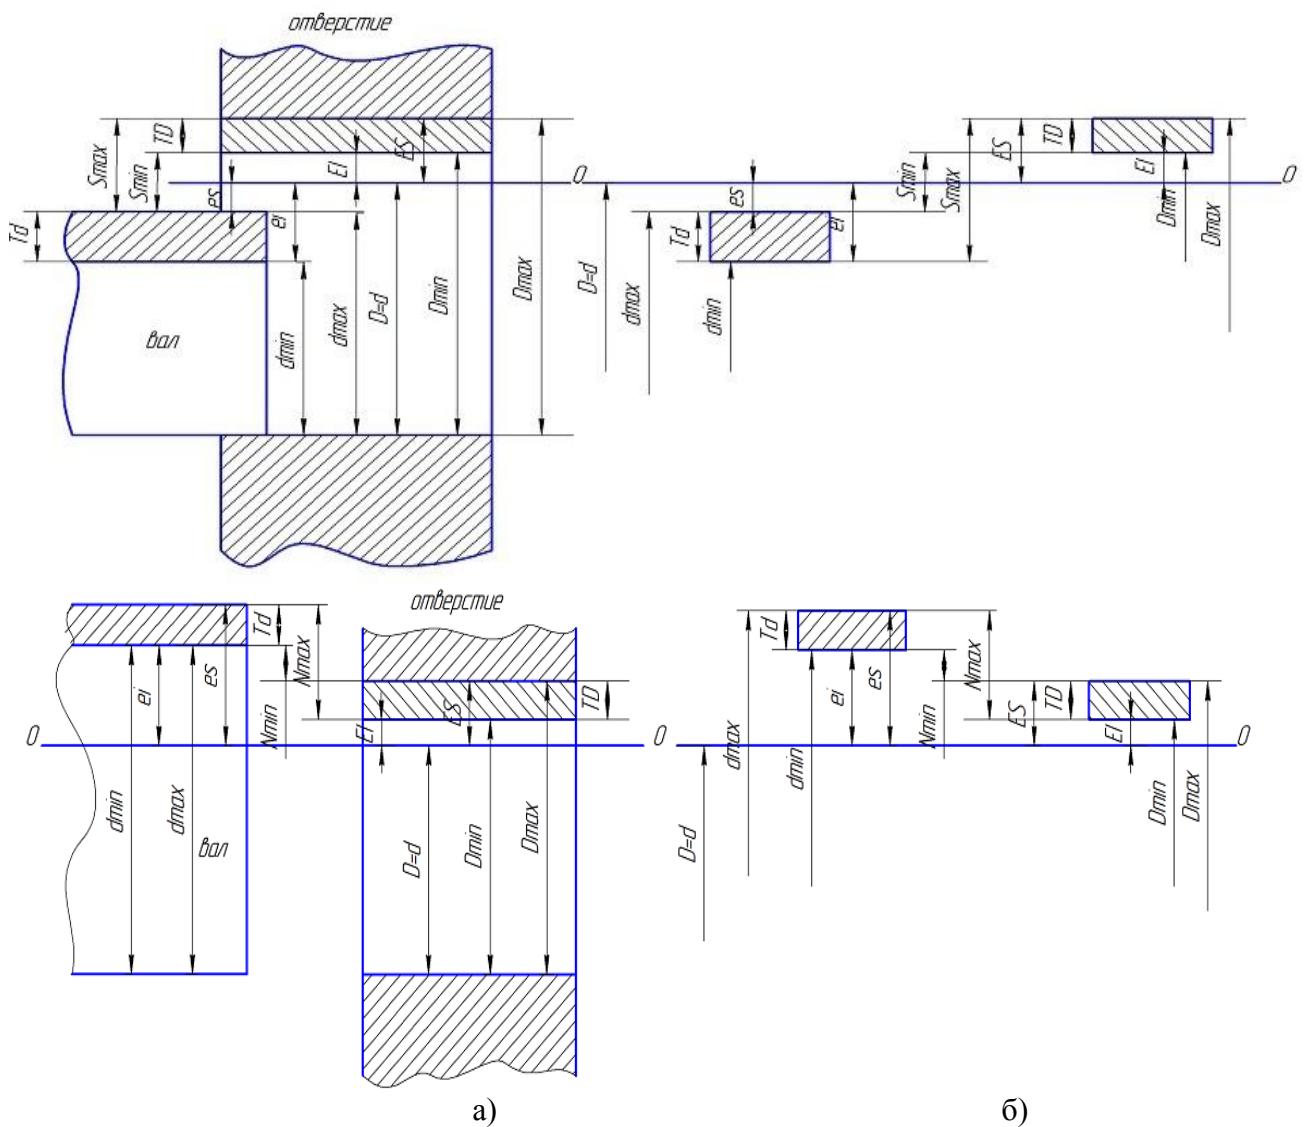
Посадка с натягом : а) схема деталей, образующих посадку (до сборки) ; б) схема расположения полей допусков
